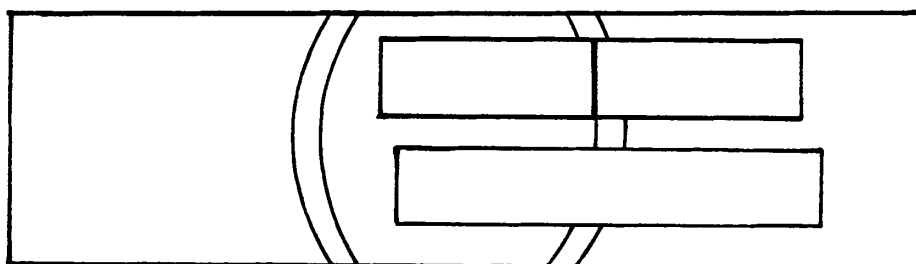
PROBETA DE ENSAYO PARA IMPACTO CHARPY DEL ACERO SAE-1030 SOLDADO POR ELECTROESCORIA SEGUN NORMA SA-370. (REF.12).
